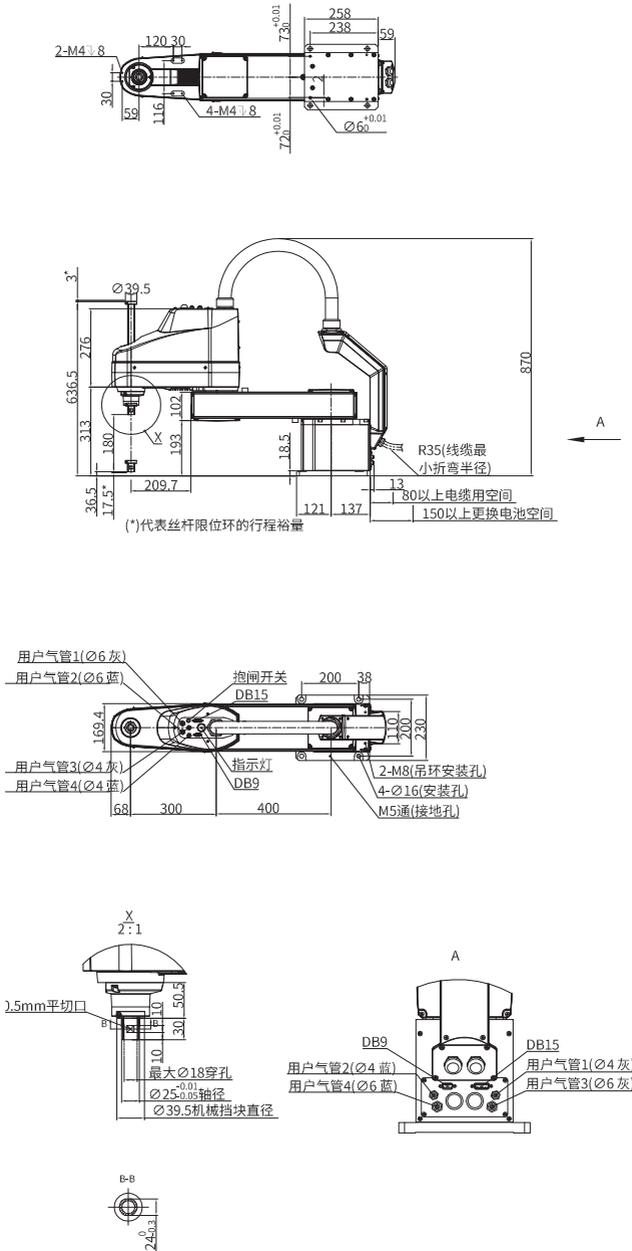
IRB111-20-70Z18TS3 安装尺寸
